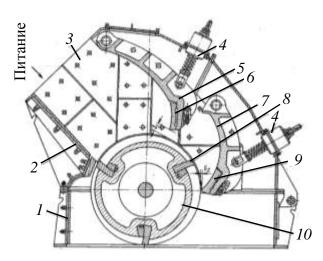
Роторная дробилка ДРК (СМД): 1 — рама; 2 — верхняя часть корпуса для загрузки исходного материала; 3 — футеровка корпуса; 4 — механизм для регулирования зазора отражательных плит; 5 и 7 — соответственно верхняя и нижняя отражательные плиты; 6 и 9 — футеровка плит; 8 — била; 10 — ротор
